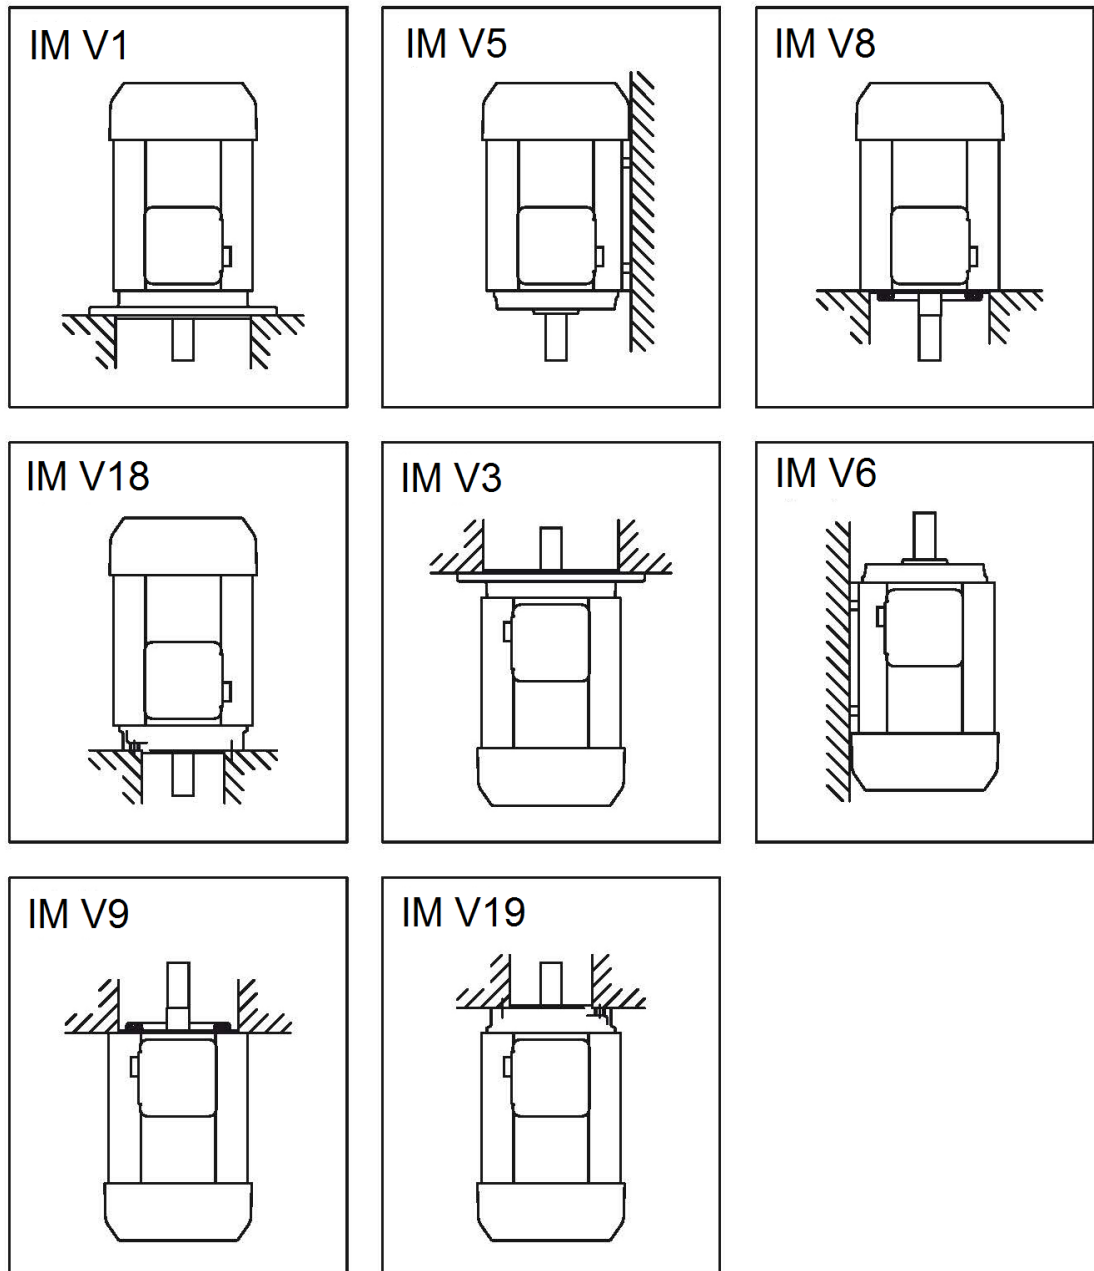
Klemmenkastenlage Flanschausführung
